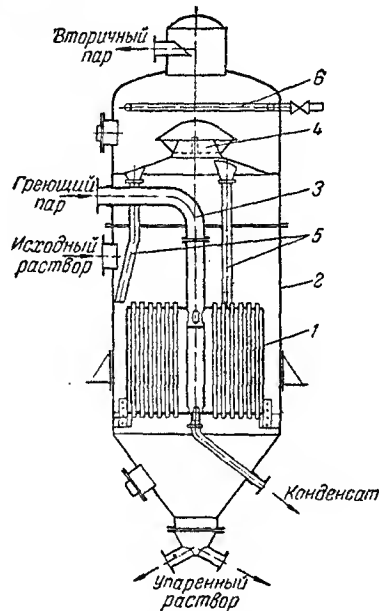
Выпарной аппарат с подвесной нагревательной камерой:
